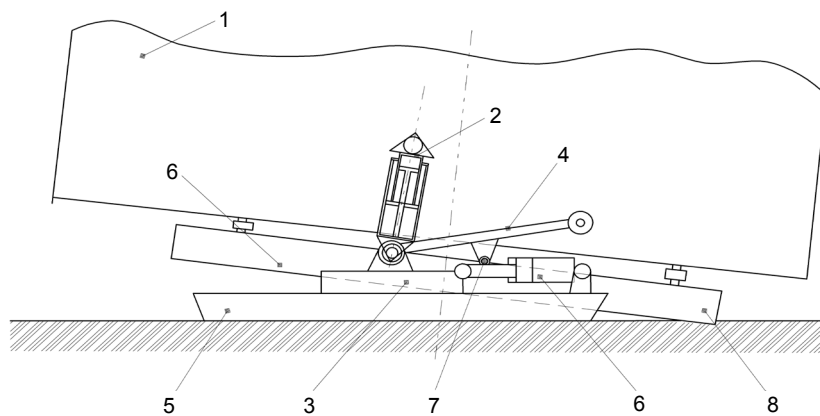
Схема механизма шагания трехопорного драглайна. 1 – кузов; 2 – гидроцилиндры подъема; 3 – скользящая опора; 4 – тяга; 5 – опорный башмак; 6 – тяговый гидроцилиндр; 7 – упор; 8 – база.
